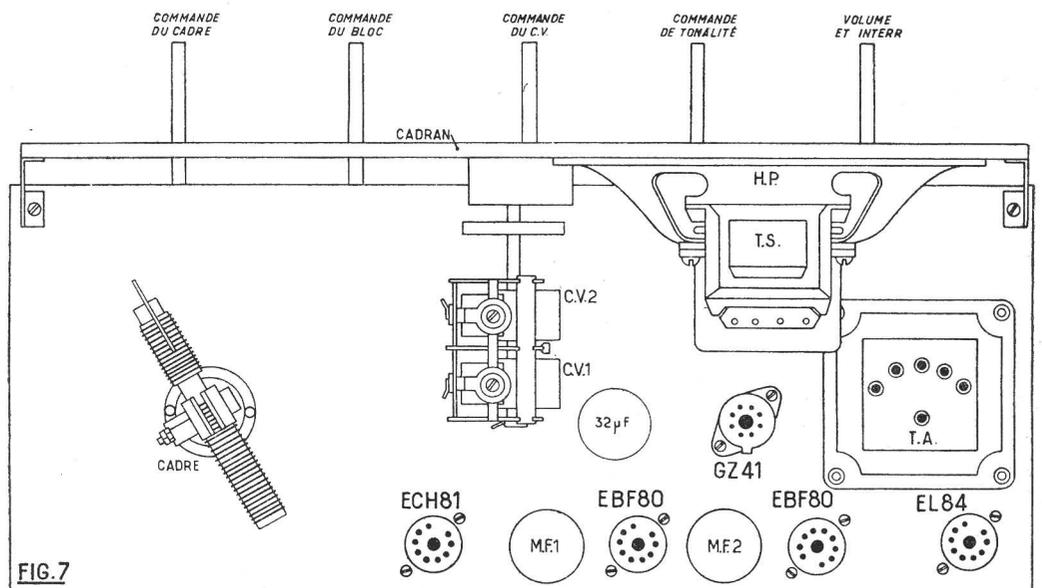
Disposition type dans un récepteur à cadre incorporé.
